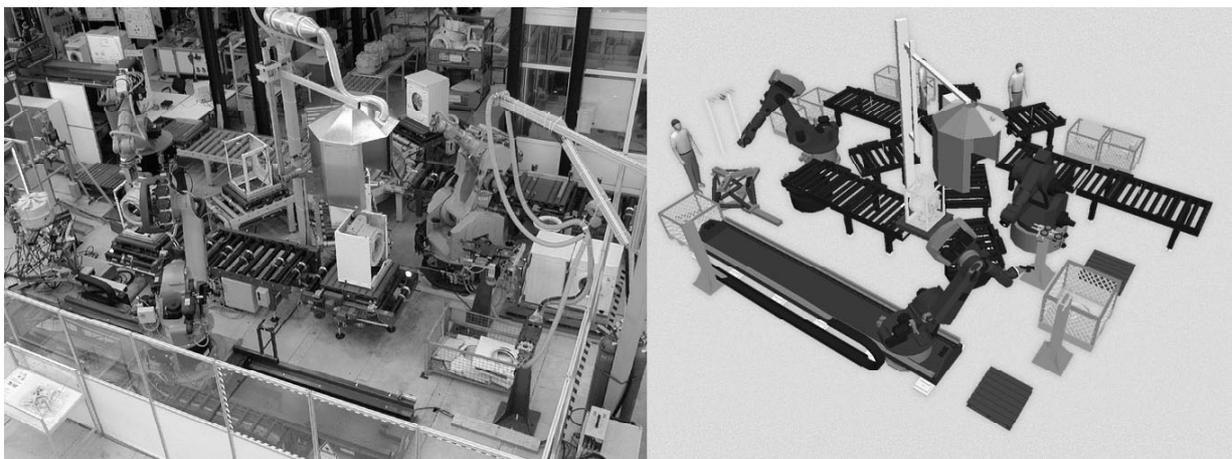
Sternlayout für die hybride Demontage Weißer Ware [CIU-03a], [KEI-00]
